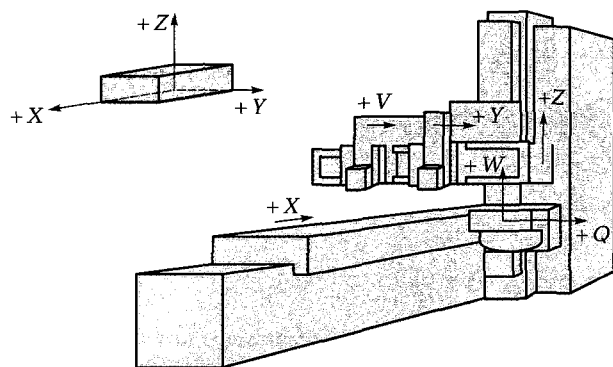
Многокоординатный станок с ЧПУ с третичным движением
